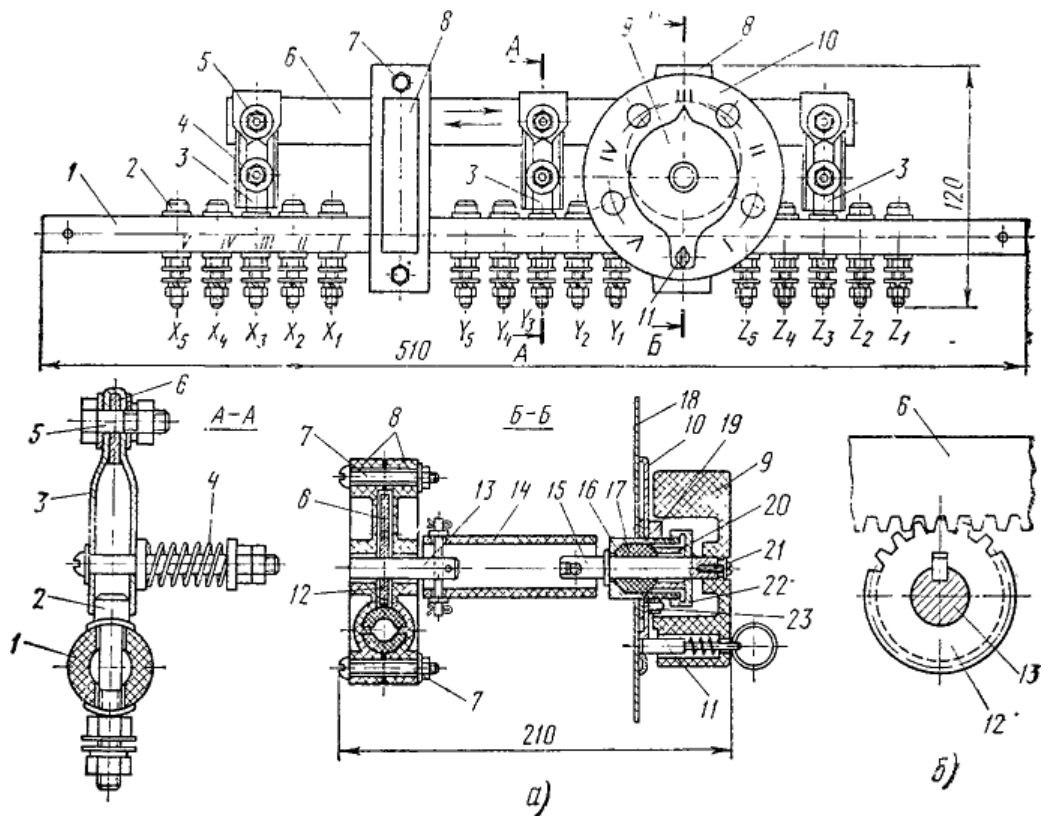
Трифазний перемикаючий пристрій ПБЗ типу ПТР-0-10/63-3-65:
